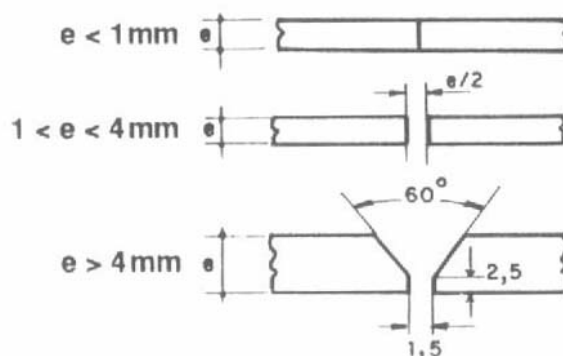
Preparação da junta para soldagem de aço inoxidável [26].
